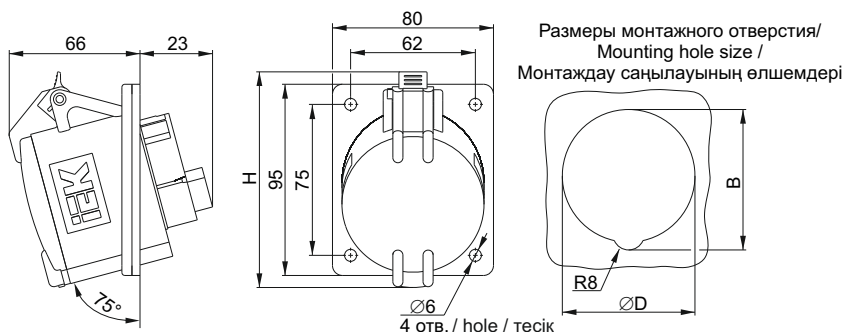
Габаритные размеры соединителей типа ССИ-145 / Figure 9 – Overall dimensions of plug and socket-outlets SSI-145 / Сурет 9 – ССИ-145 типті жалғастырғыштардың габариттік өлшемдері
